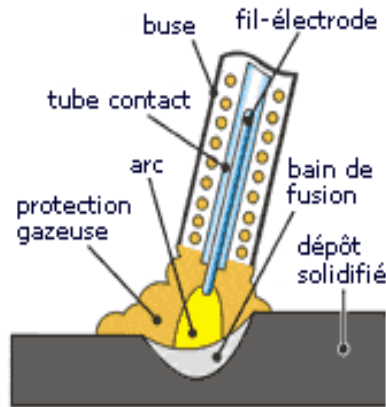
Schéma d'assemblage par soudage .
